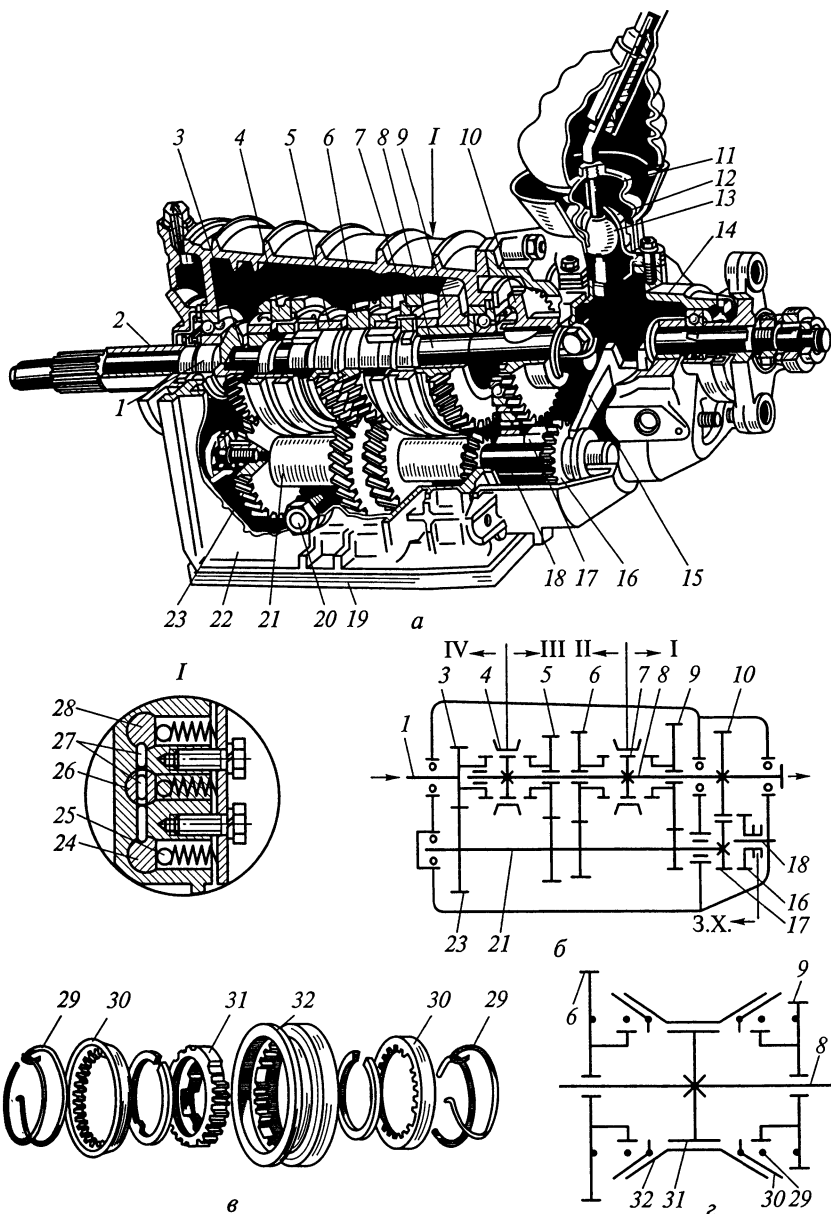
Коробка передач легковых автомобилей ВАЗ:
